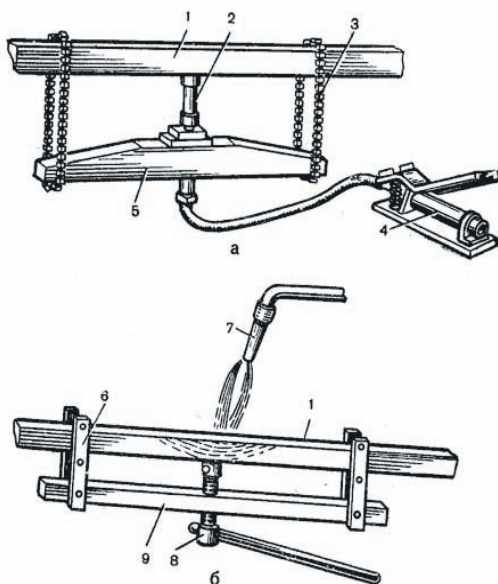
Правка рамы: а – гидравлическое приспособление б – винтовое приспособление; 1 – деформированный участок рамы; 2 – шток силового цилиндра; 3 – цепь; 4 – гидропривод; 5 – траверса; 6 – скоба; 7 – наконечник горелки; 8 – винт; 9 – брус.
